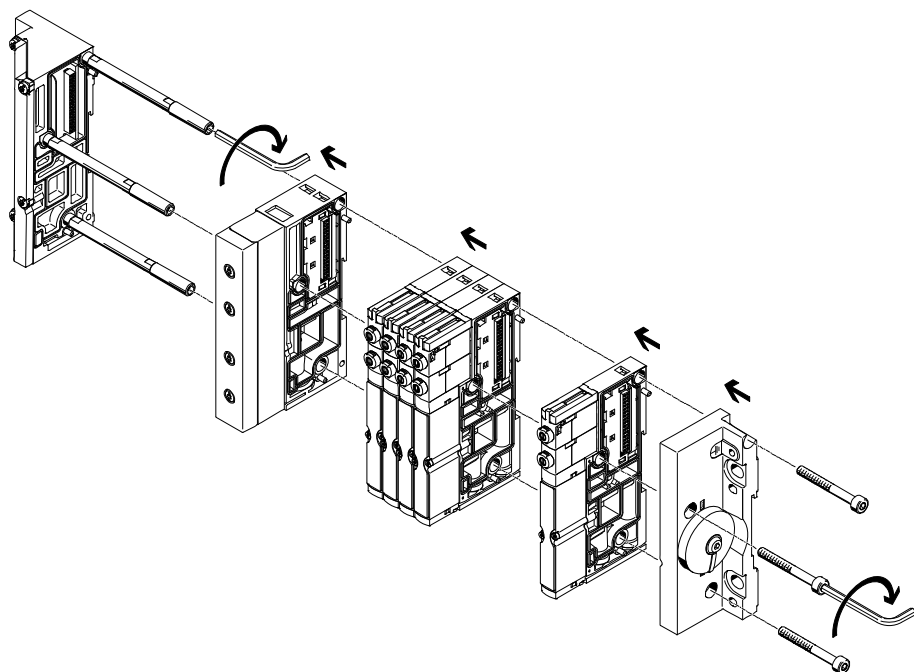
Verschraubung der Anschlussplatten mittels Zuganker
